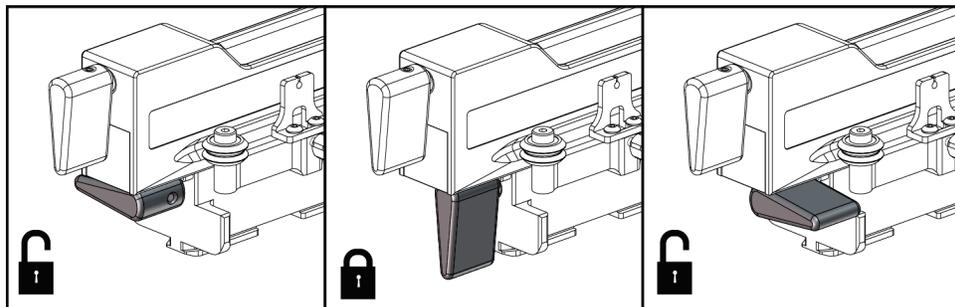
Posições travada e destravada da alavanca do suporte do dispositivo
